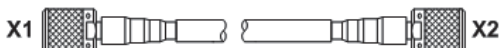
Кабельная сборка с двумя кабельными резьбовыми соединителями
